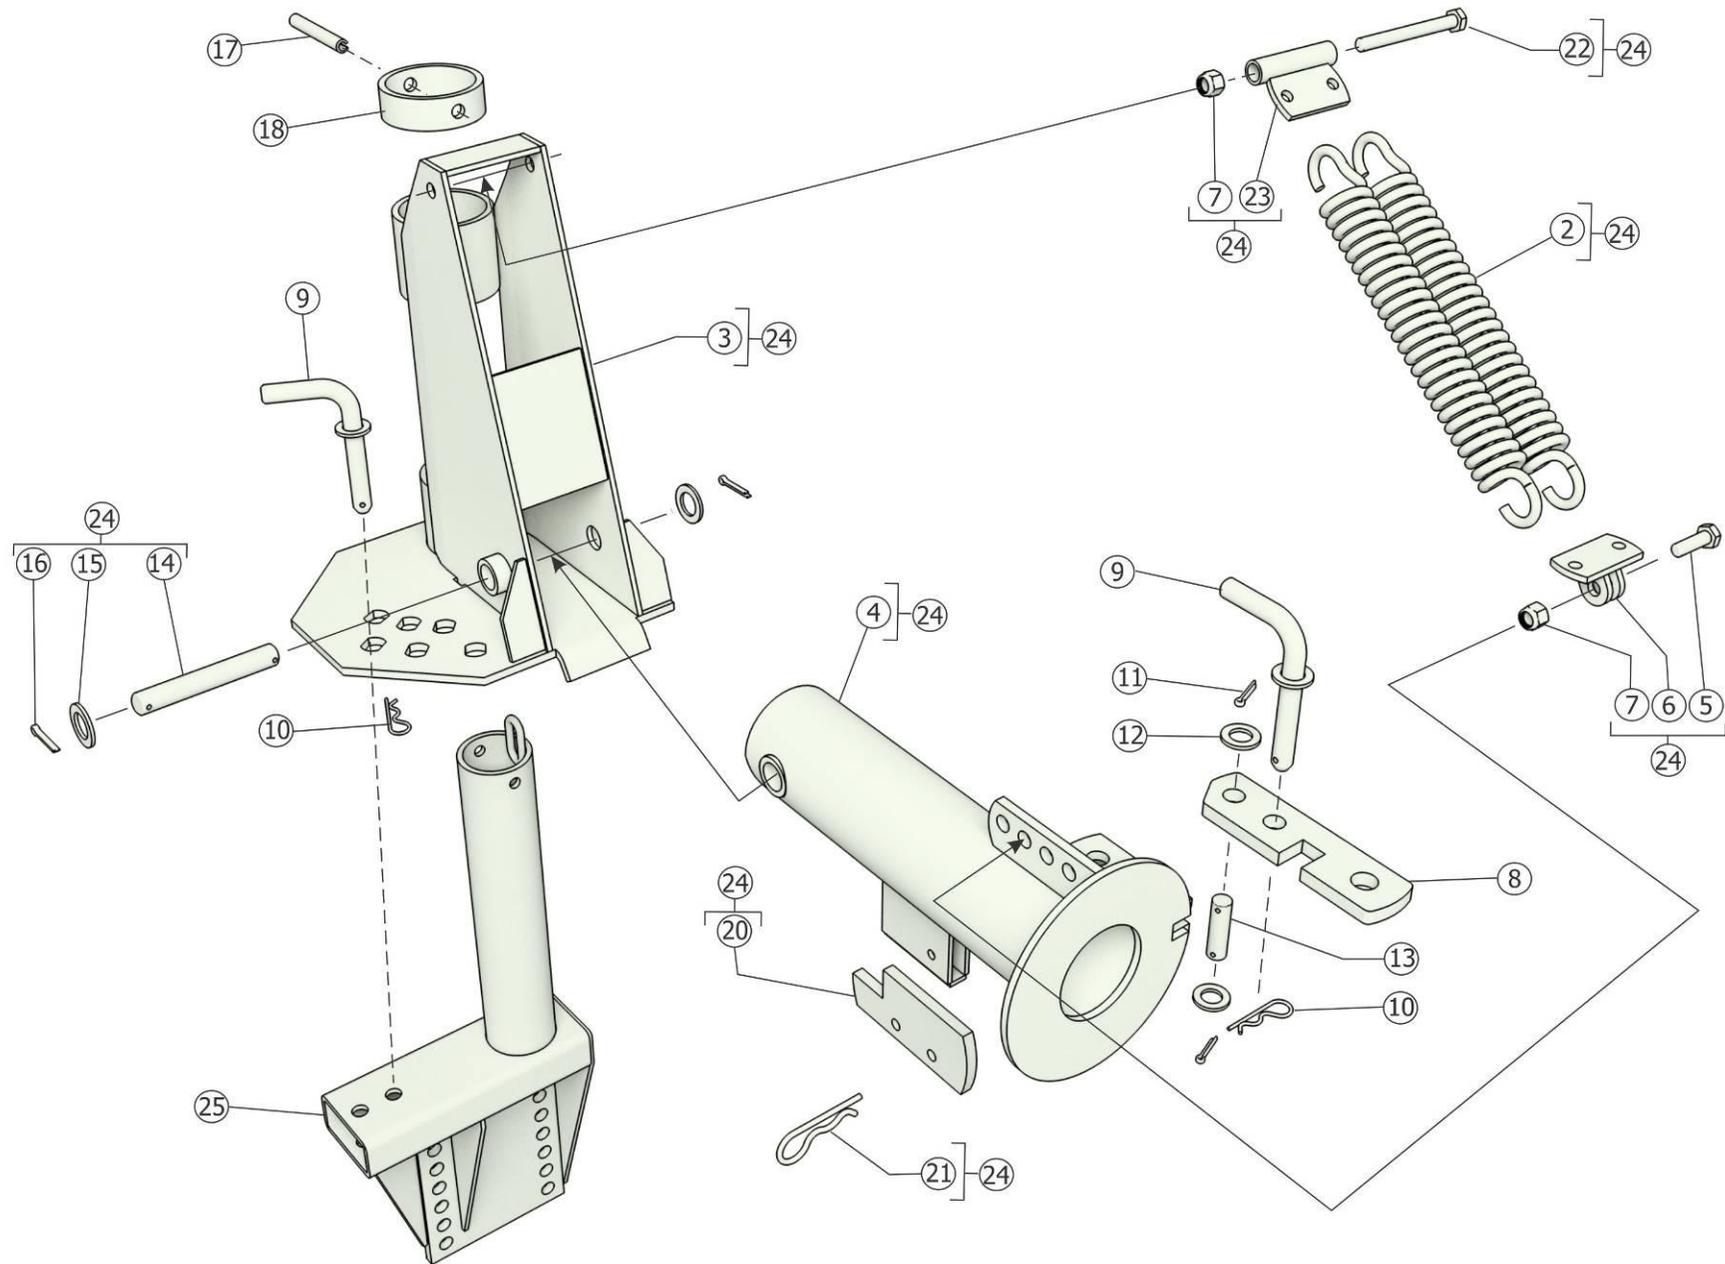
Стойка поворотная ГП-601.03.000-01
